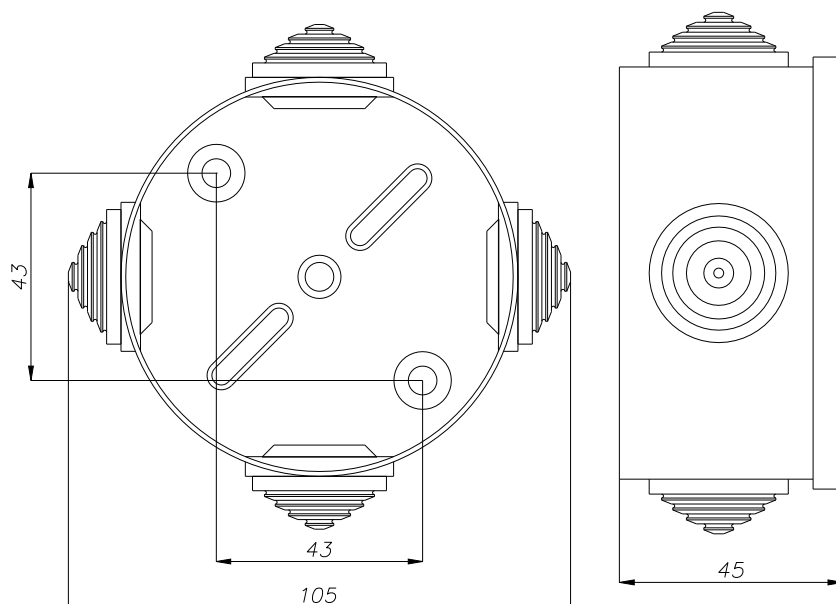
Габаритные и установочные размеры разветвителя КРИ-4.
